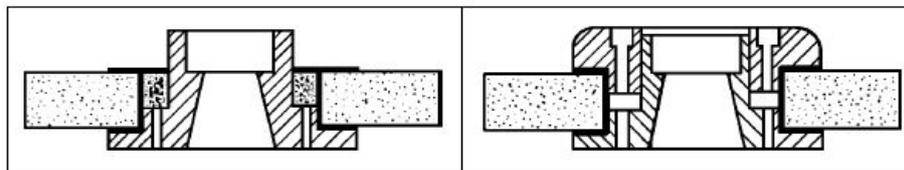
Flange para fixar o disco, fonte – SENAI
